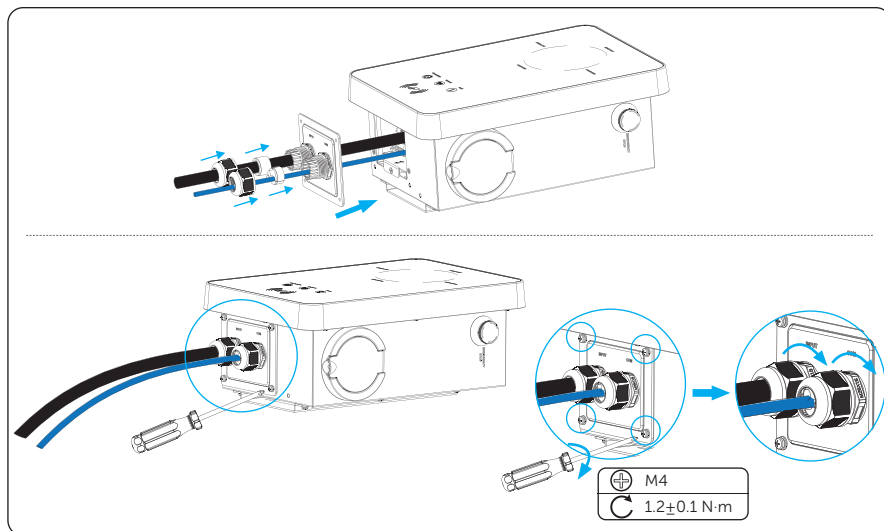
Befestigen der rückseitigen Abdeckung
